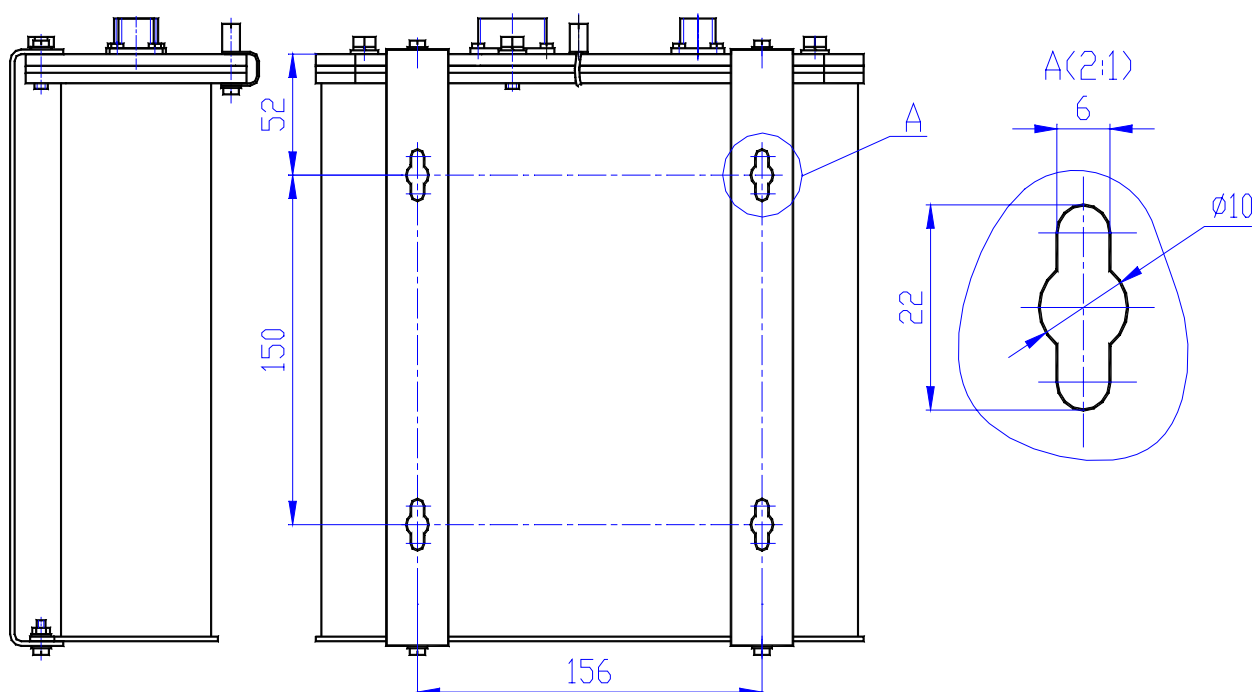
Разметка стены для установки блока в герметичном корпусе.
